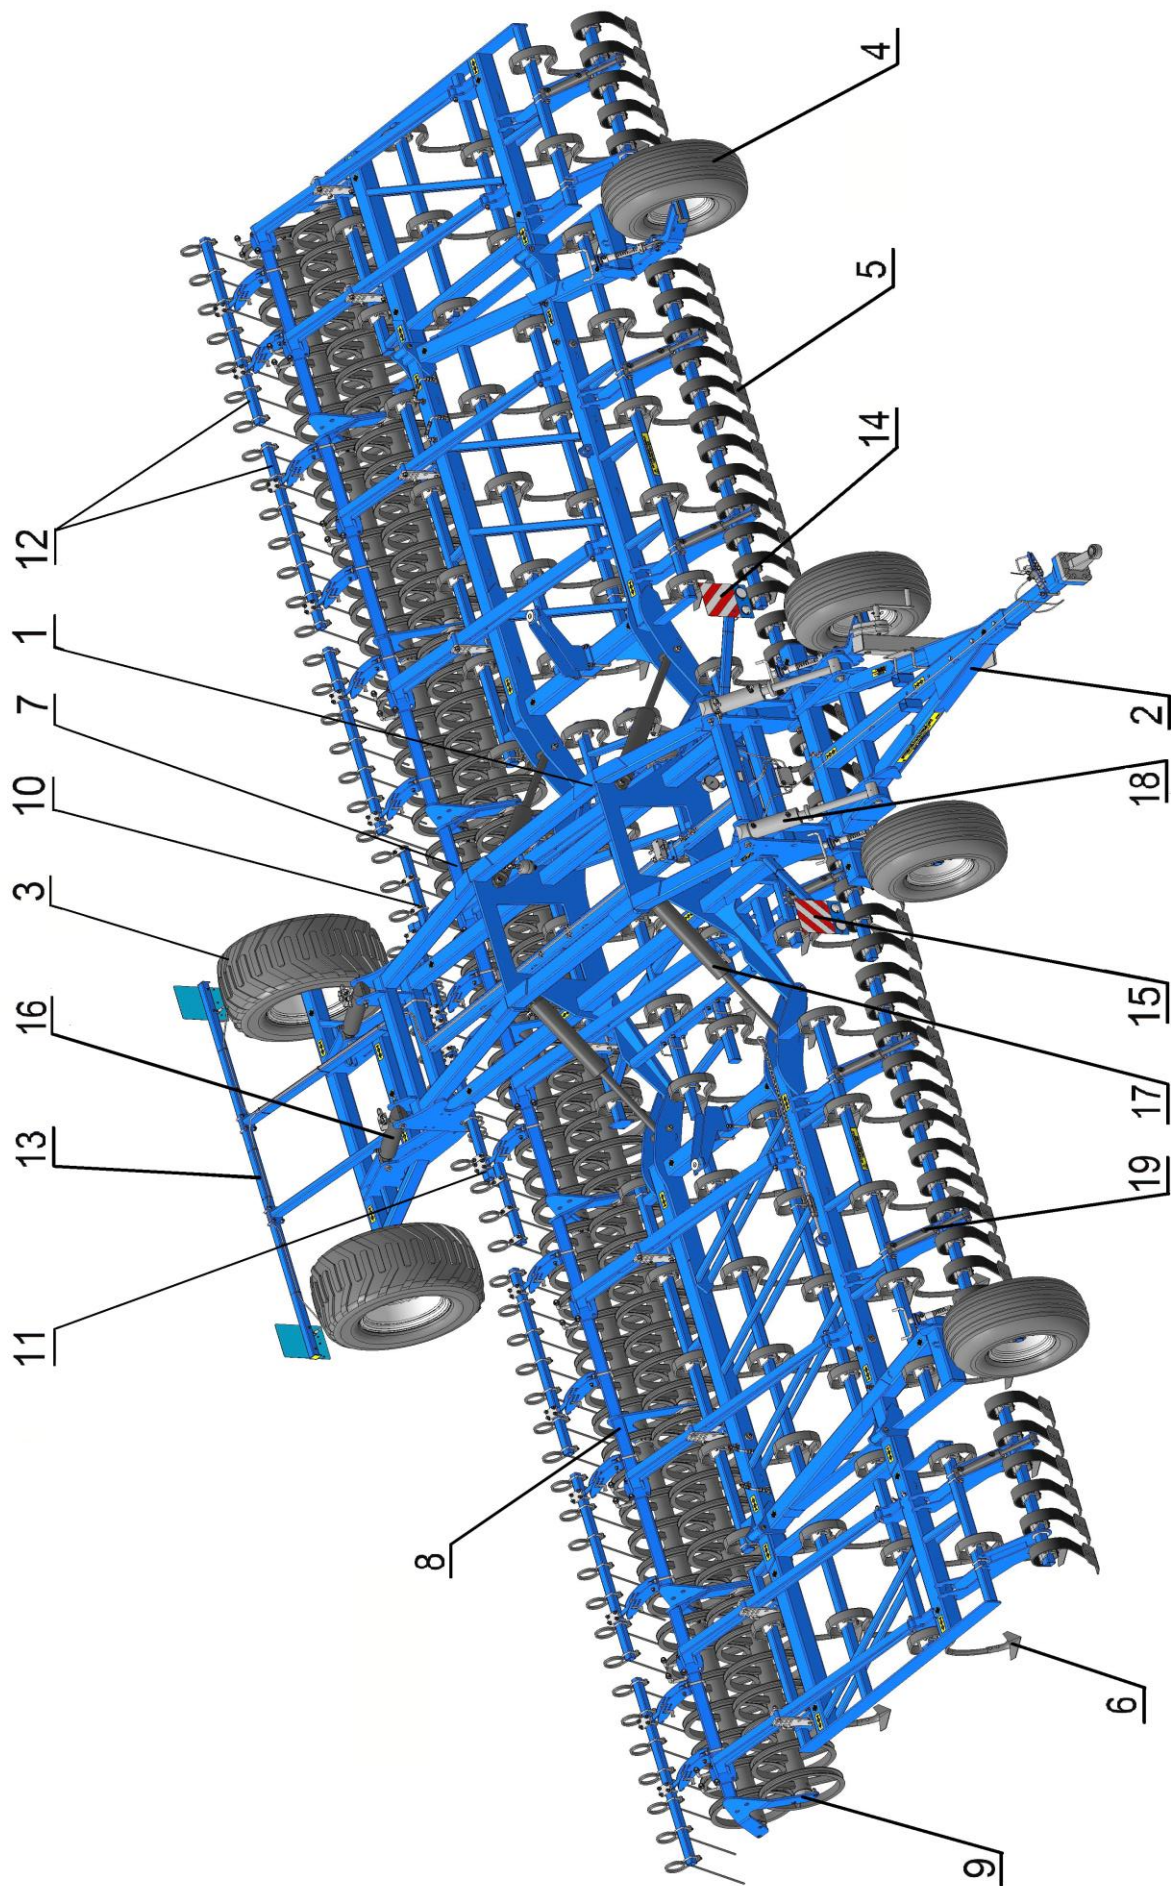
Культиватор прицепной универсальный КПУ-12 (в рабочем положении)
